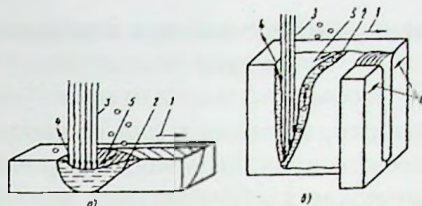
Схема электронно-лучевой сварки металлов малой (а) и большой (б) толщины:
